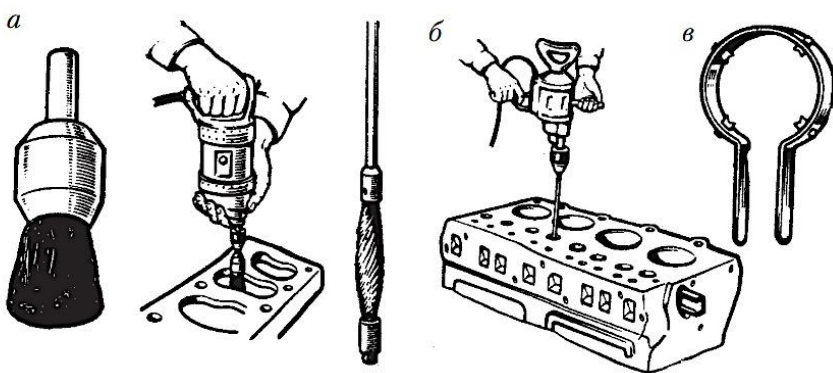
Приспособления для удаления нагара и других отложений [39]:
